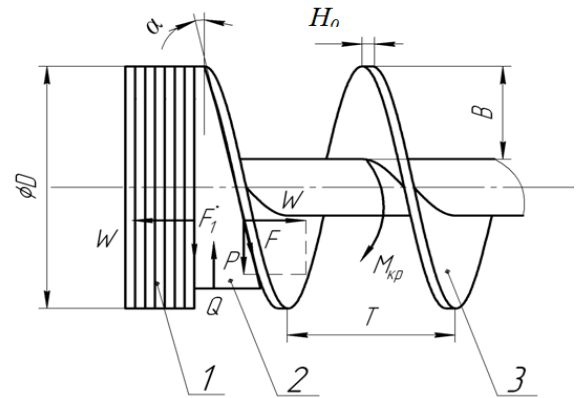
Розрахункова схема пристосування для калібрування витка гвинтової заготовки на крок: 1 – щільно навіта заготовка, 2 – клин, 3 – калібровані витки гвинтової заготовки
